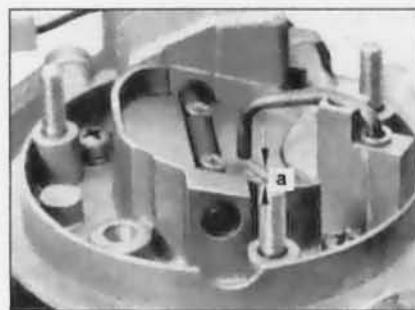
Установочный зазор трубы обогащена. карбюратора 1B3 (Глава 10)
